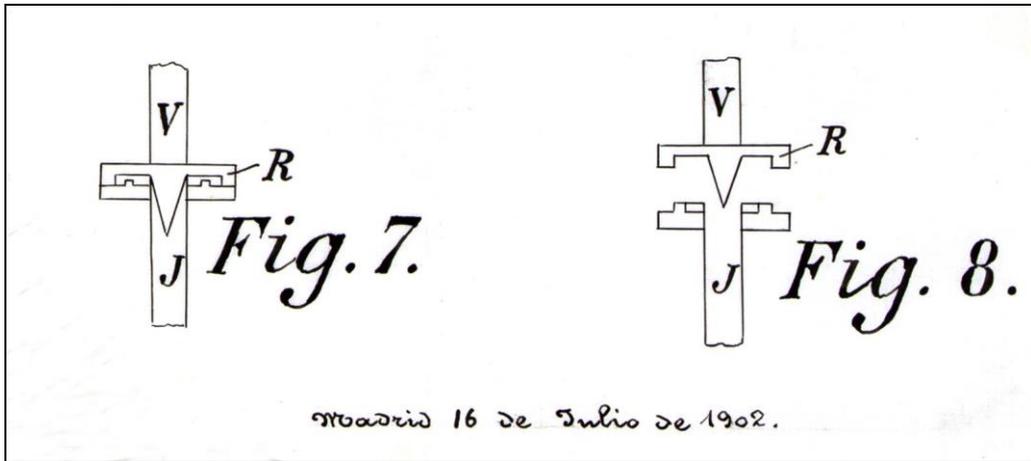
Detalle de la válvula de goteo (Arch. J.M. Sanchis)
